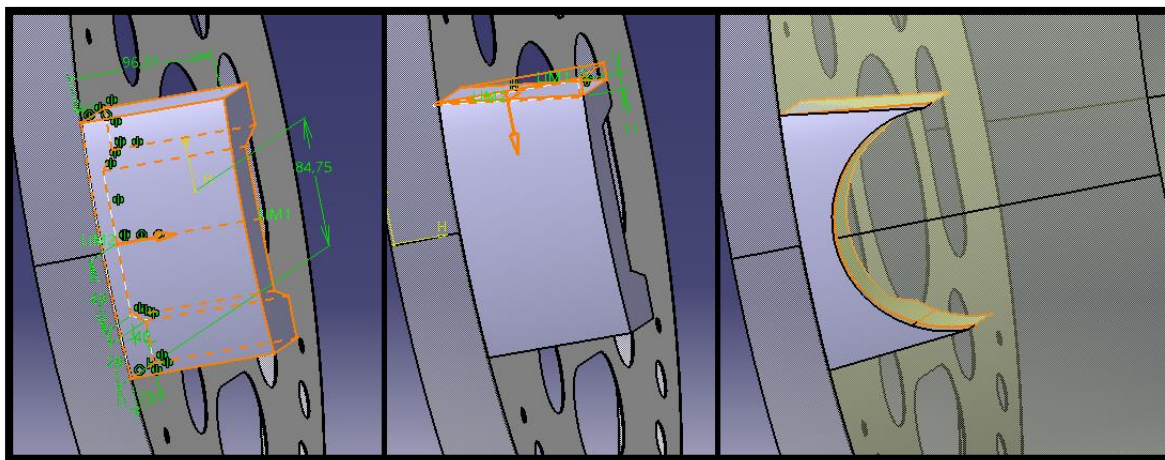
Spinner: Operaciones Pad, Pocket y Trim del 2º componente de la pieza 1
